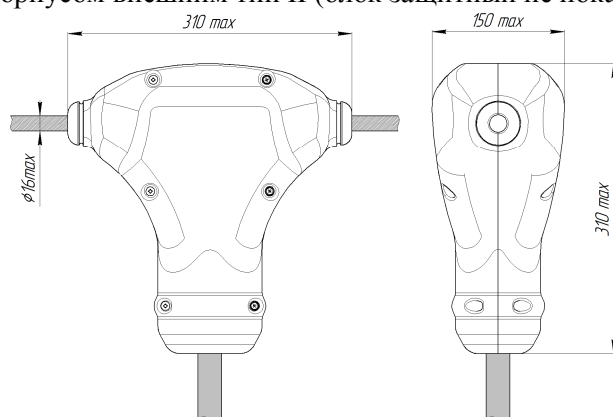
Габаритные, установочные размеры ДИЭ
